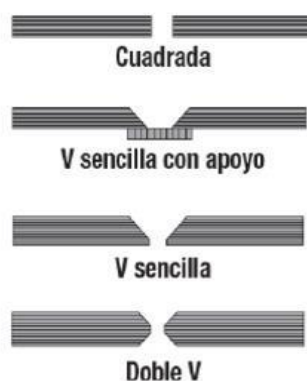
Tipos de uniones soldadas a tope
